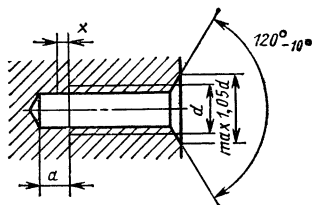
Форма сбega и недореза для внутренней метрической резьбы
